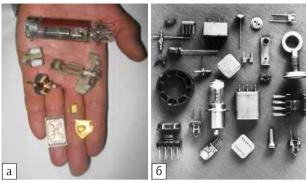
Изделия, выполненные: a) микроконтактной сваркой, б) микроплазменной сваркой и пайкой
